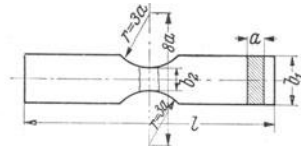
Stabform zur Ermittlung der Festigkeit des Schweißgutes.
